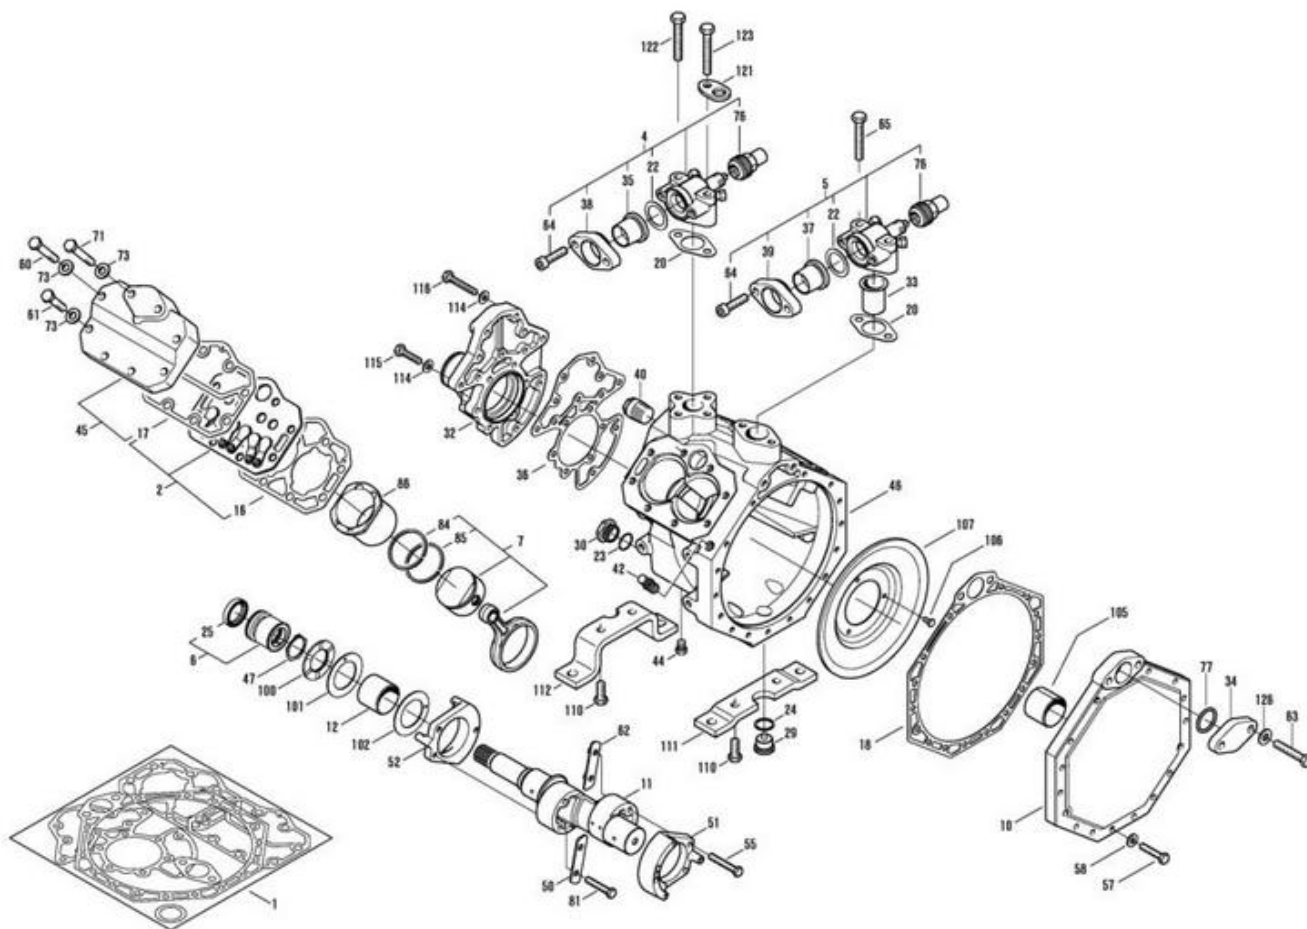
Desenho dos componentes de um compressor Bitzer.
